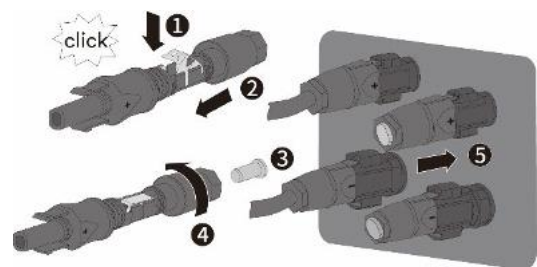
Setzen Sie die DC-Steckverbinder ein und verschließen Sie ungenutzte Steckverbinder
